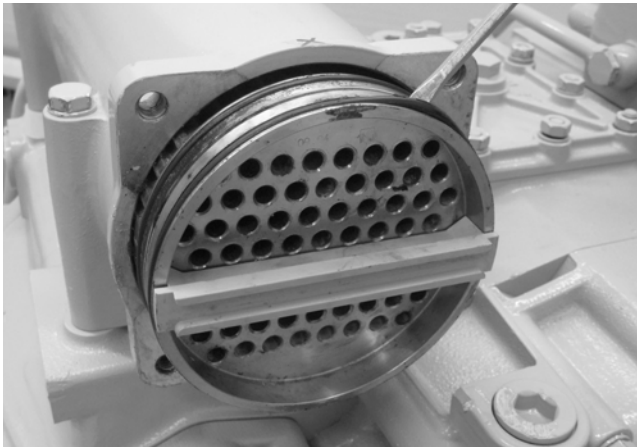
Demontage des äußeren O-Rings (Beispiel)
